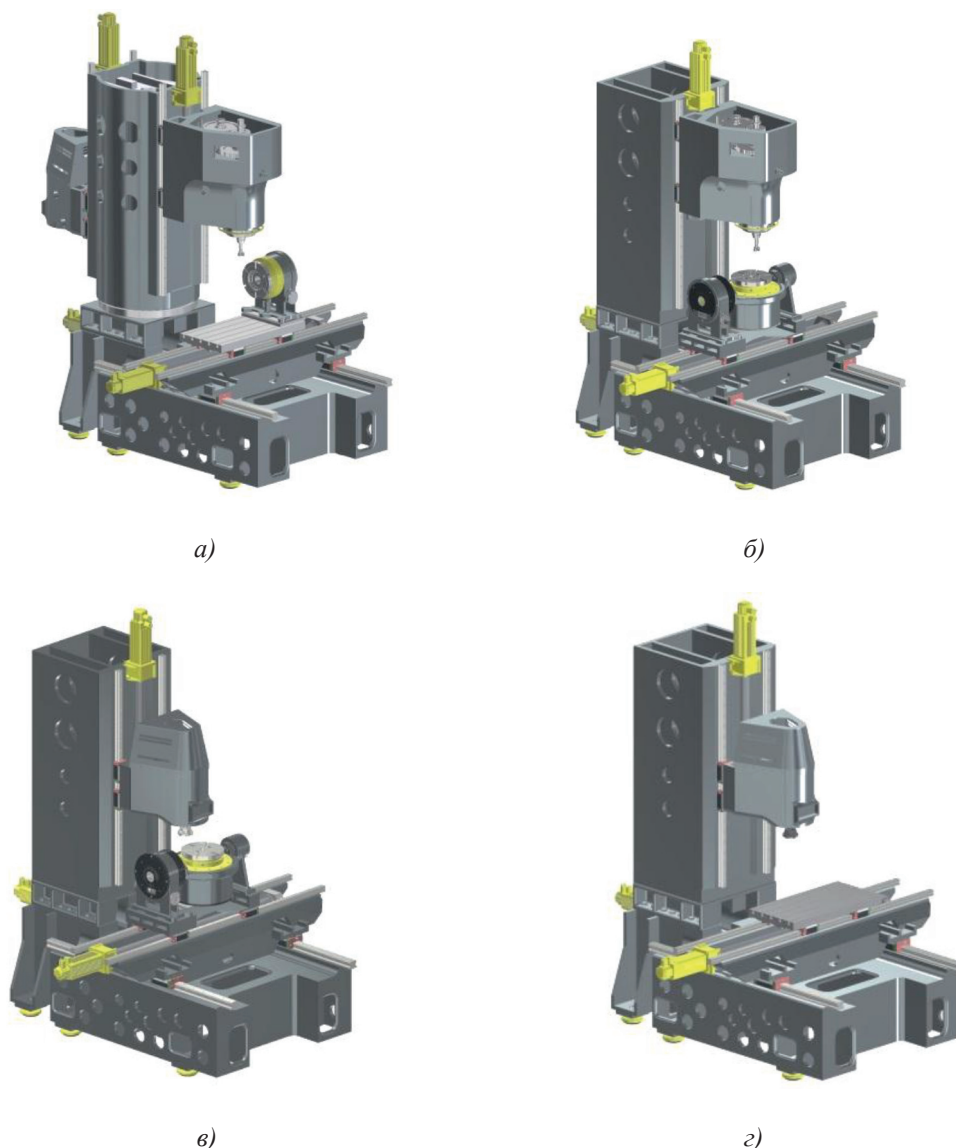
Модульные компоновки: а) двухшпиндельный станок с поворотной стойкой и вертикальным поворотным столом; б) пятиосевой станок для силового резания; в) пятиосевой станок для скоростного резания; г) трехосевой станок для скоростного резания
